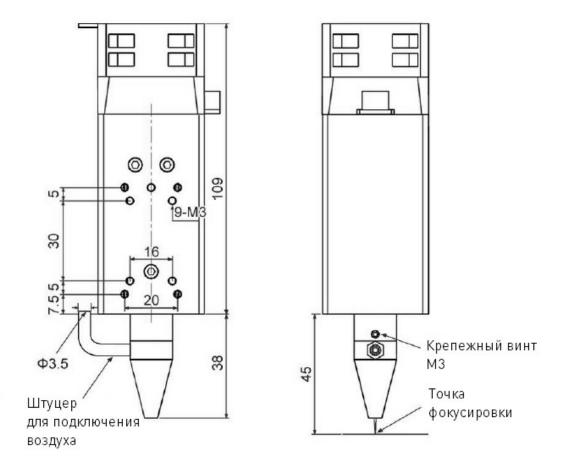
Габаритный чертеж лазерного модуля LT5W-12V.
